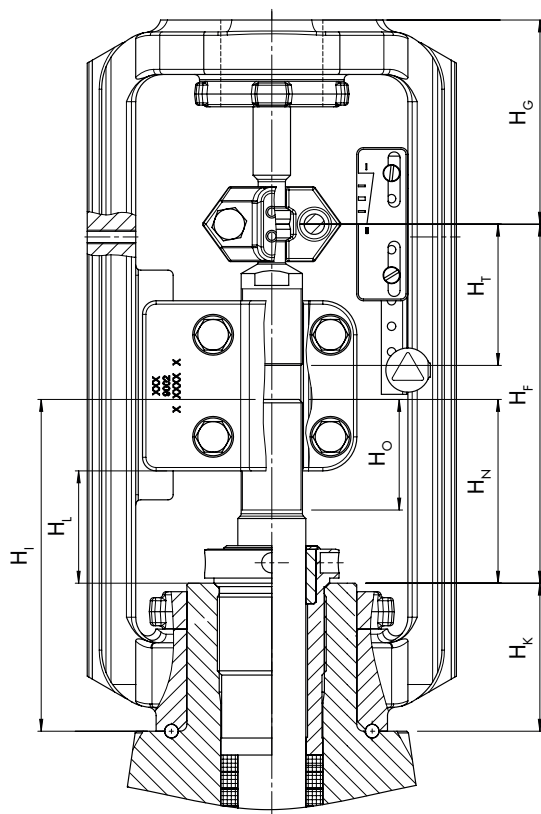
Габаритный чертёж с установочными размерами для пневматических приводов Тип 3271 и 3277
